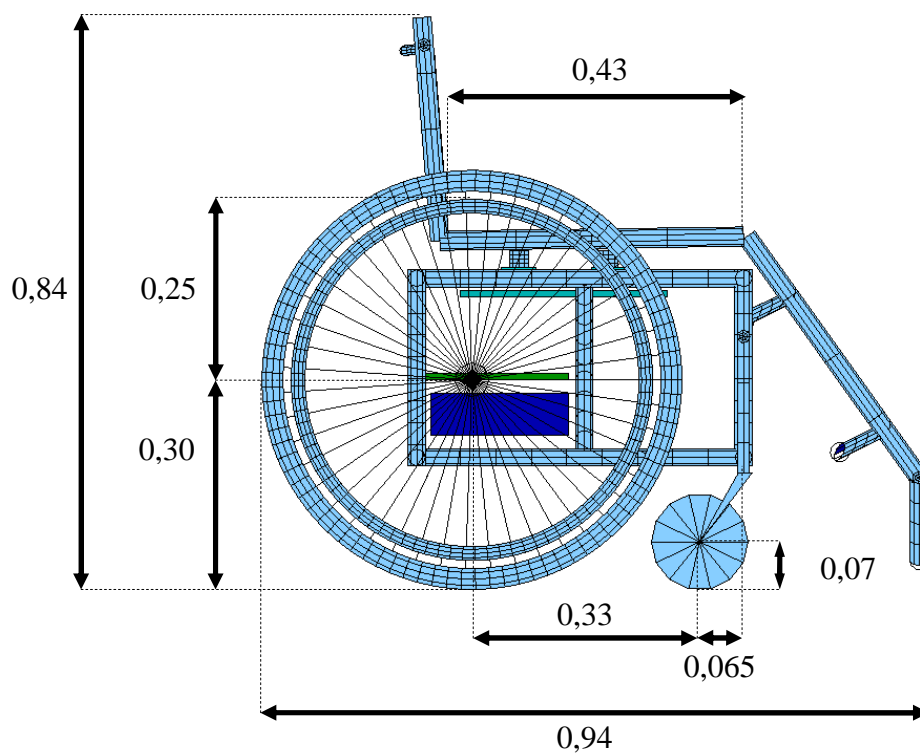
Principales dimensions du FRET-1 vu de profil. (en mètres)
